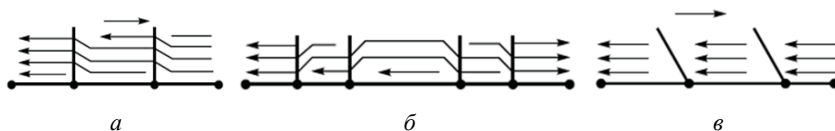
Способы заполнения разделки кромок при многослойной сварке:
